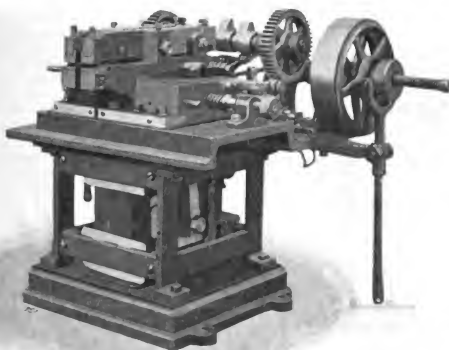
Automatischer Schweissapparat Type 2A mit mechanischem Antrieb.
